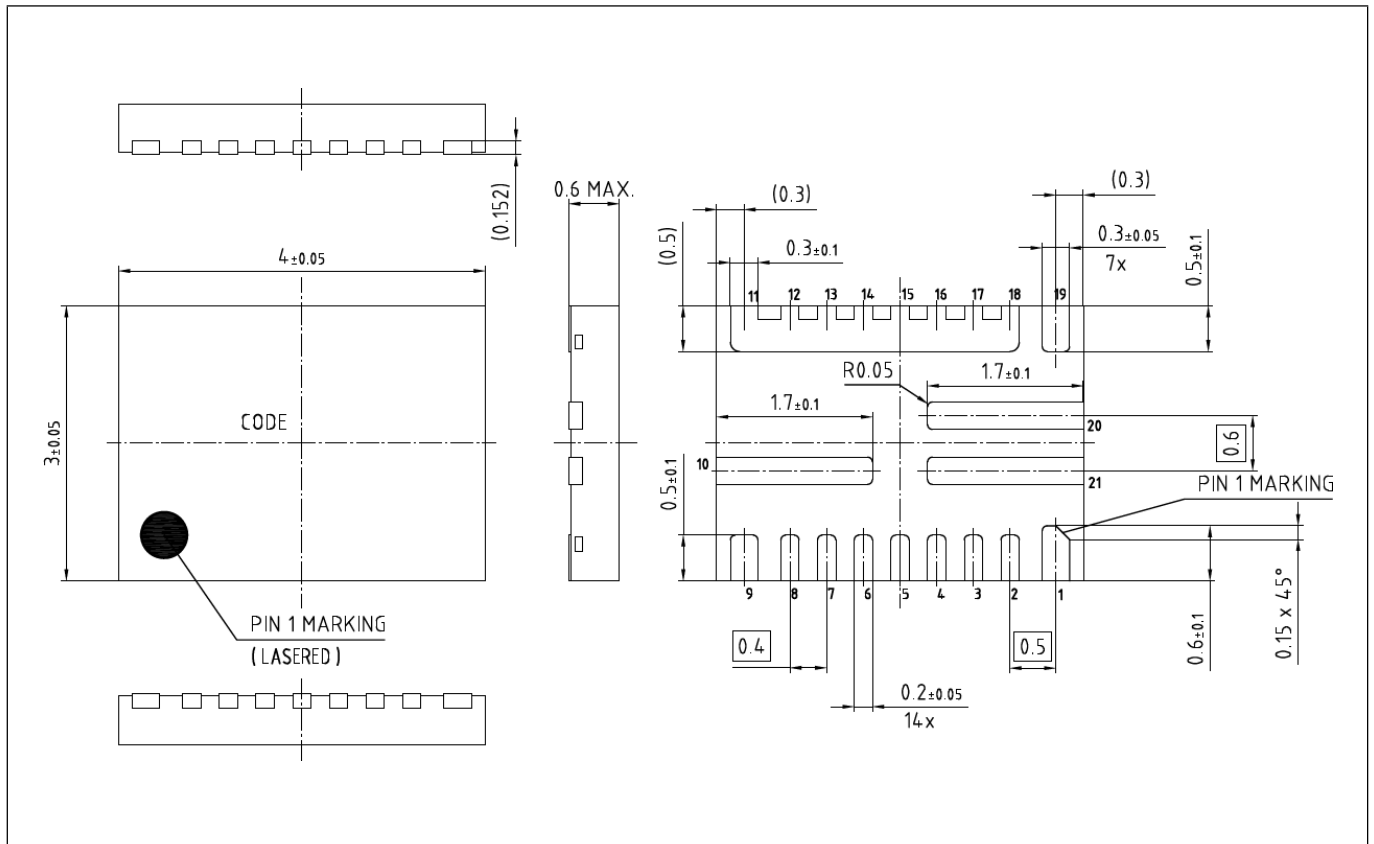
封装尺寸 (所有尺寸均以毫米为单位)
